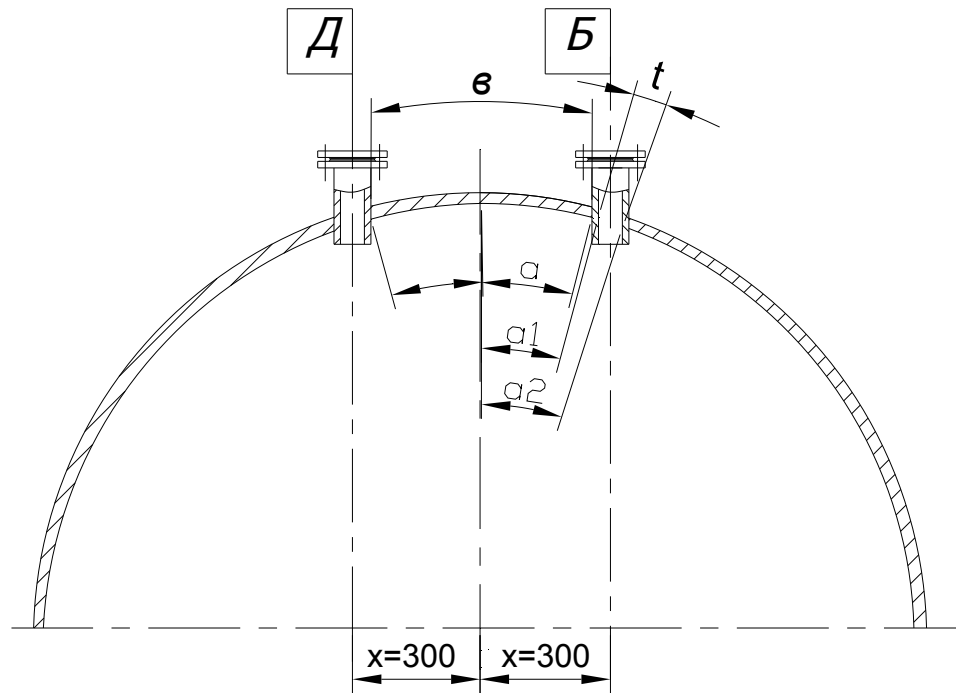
Розташування штуцерів Б і Д на циліндричній обичайці корпусу.
